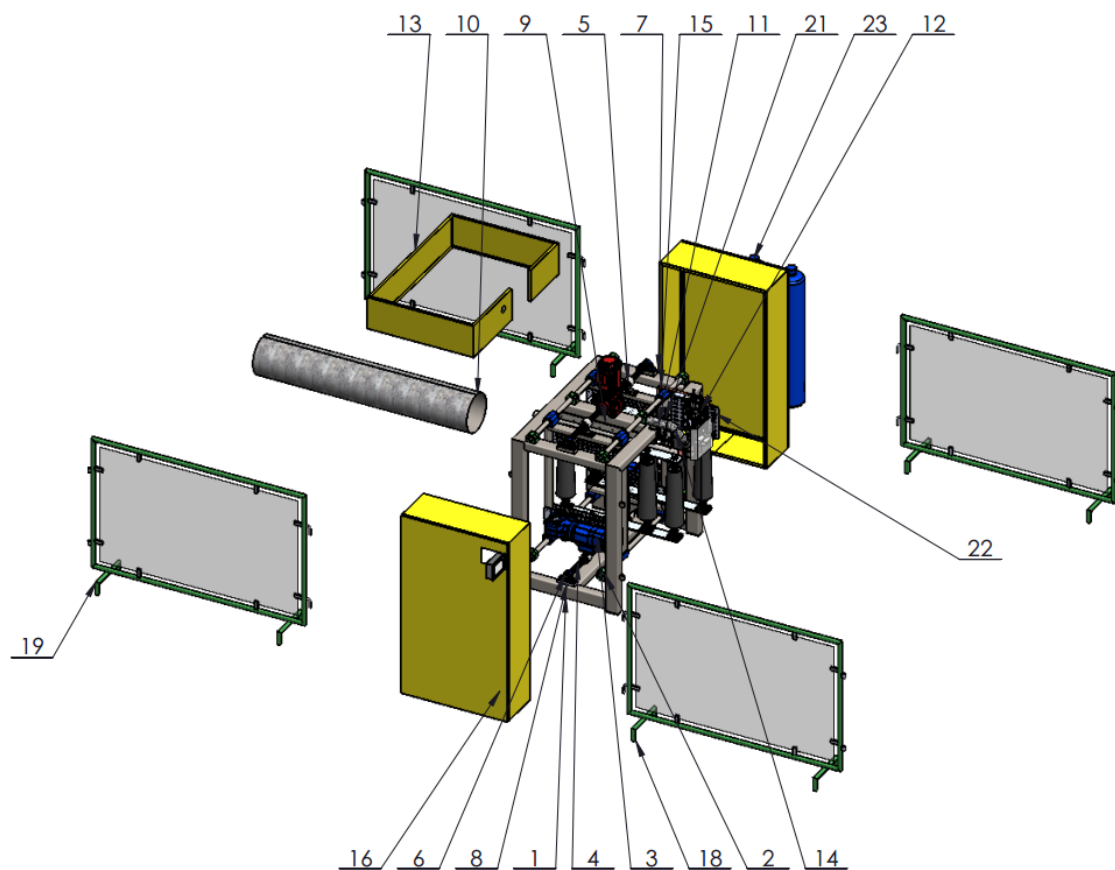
Equipamento de soldadura completo, representado em vista isométrica explodida e assemblada
